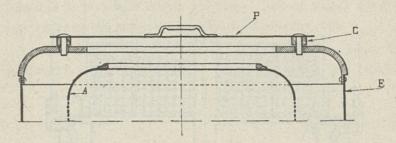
Protecteur du panier d'une essoreuse-toupie.
